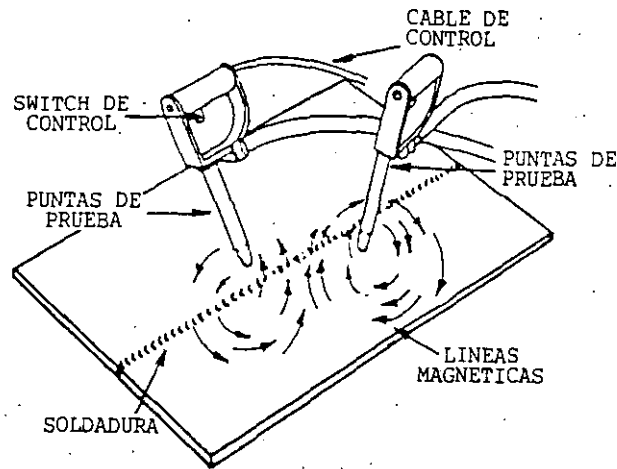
FIG. CAMPO MAGNETICO CREADO ALREDEDOR DE UNA SOLDADURA. LA CORRIENTE PASA A TRAVES DE LA SOLDADURA ENTRE LAS DOS PINZAS DE PRUEBA.
